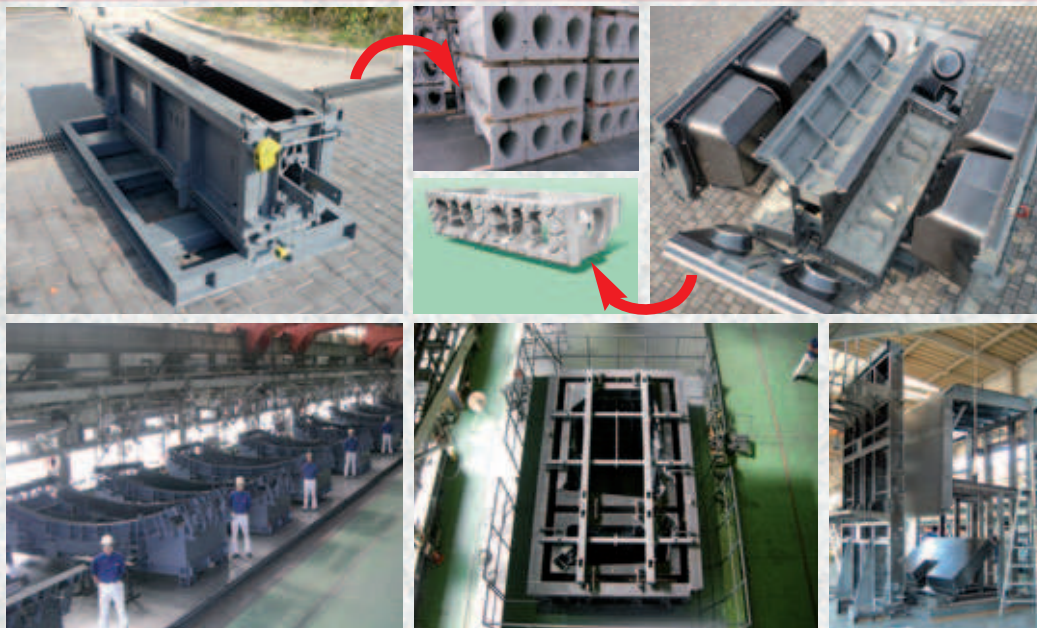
Conduite de drainage pour les eaux d'écoulement
